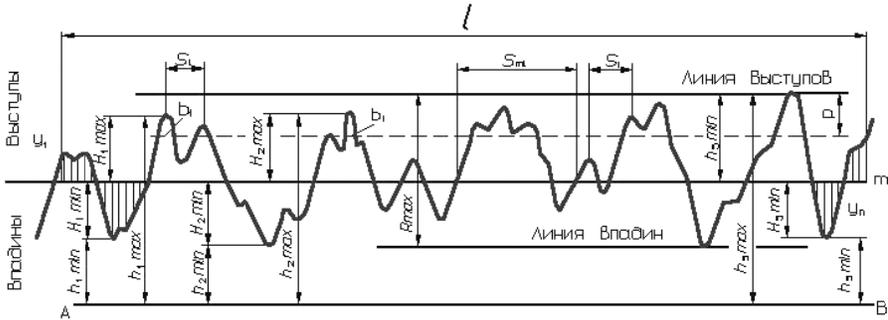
Параметры шероховатости обрабатываемой поверхности
